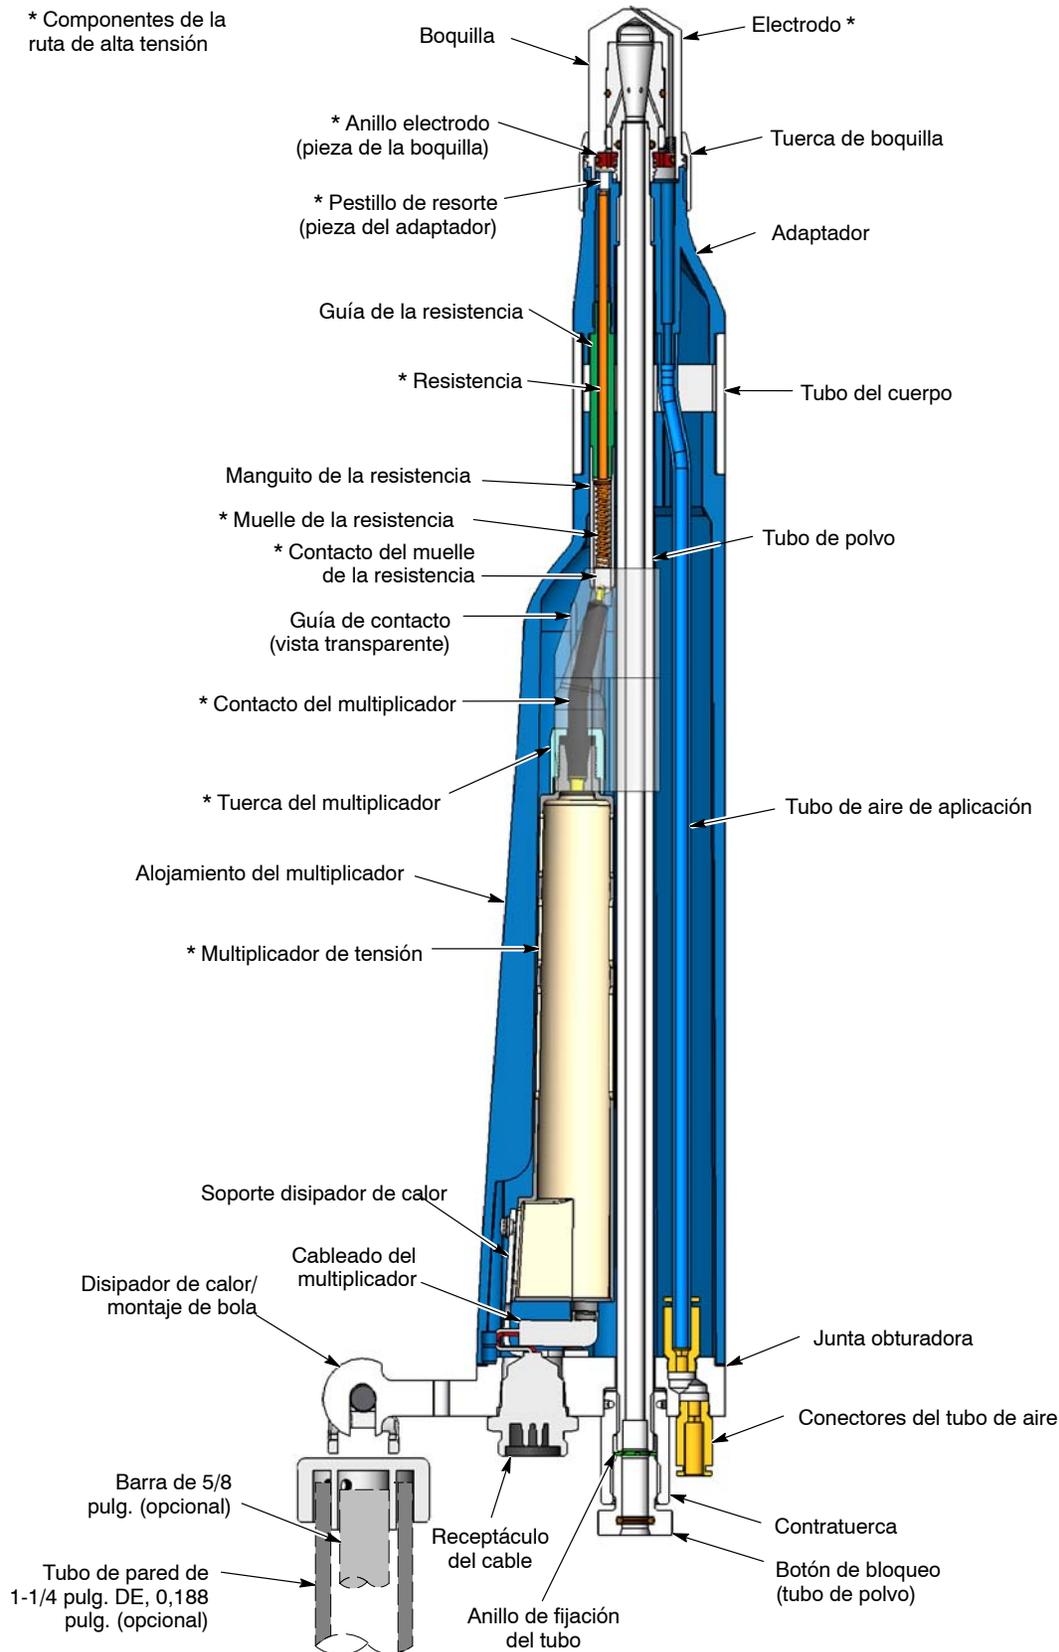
Vista transversal – Componentes y montaje de la pistola de montaje en barra
